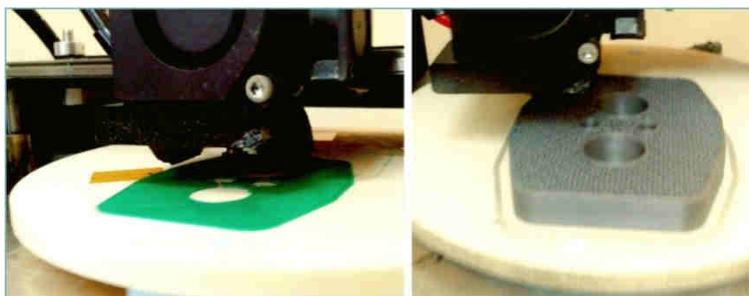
Печать пластинчатых деталей ABS- и PLA-филаментами на готовом устройстве без подогрева стола
